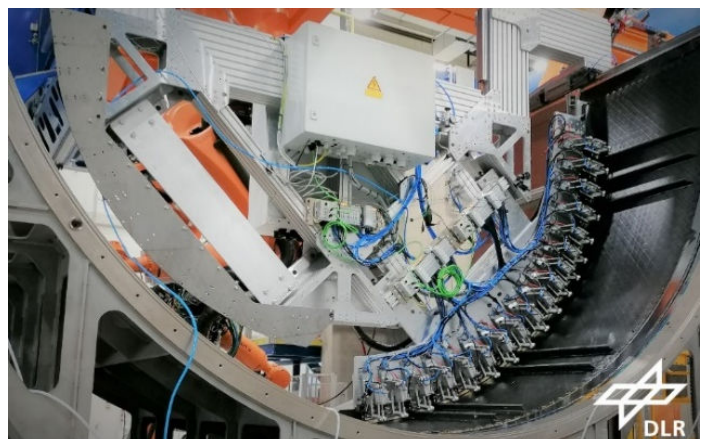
Schweißbrücke für die Integration eines Spantes
